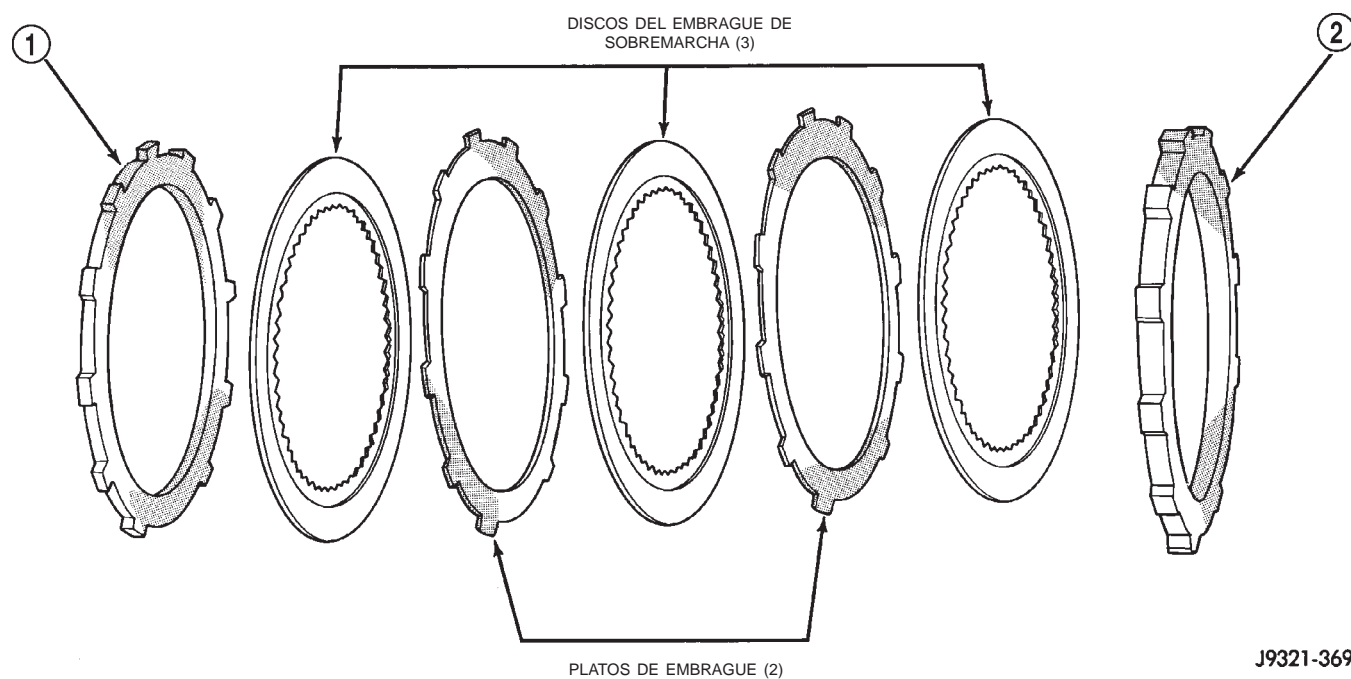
Componentes del embrague de sobremarcha de la 42RE
